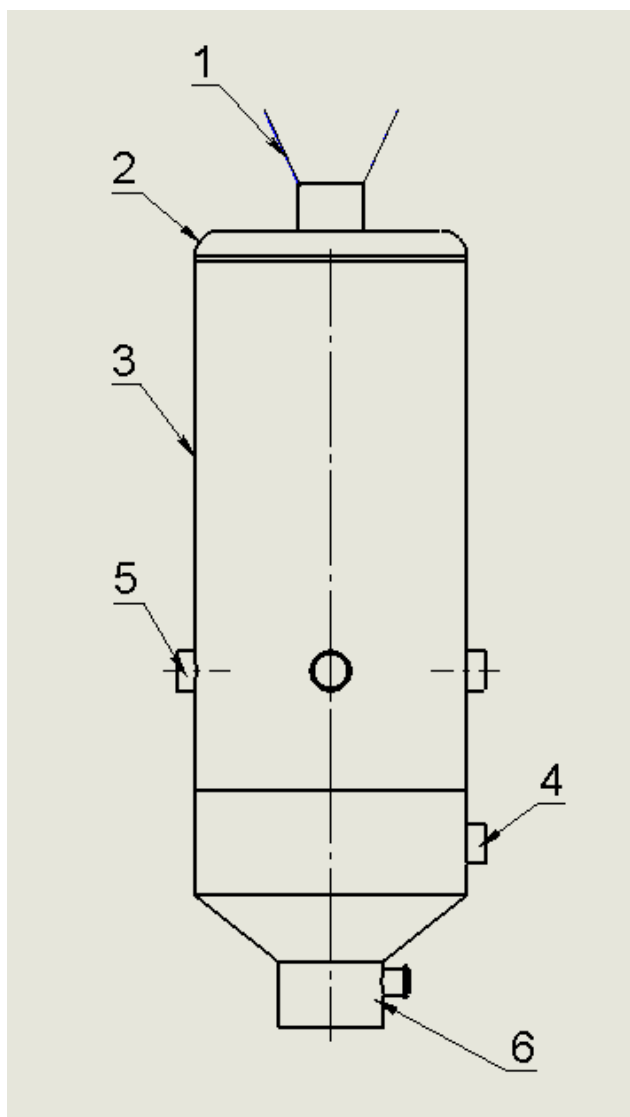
Технологическая схема реактора для переработки сорбированных нефтяных шламов: 1- патрубок для подачи сорбированных нефтешламов, 2 – крышка, 3- корпус, 4 – патрубок для отвода газа, 5 - патрубки подачи воздуха, 6 – зольник
